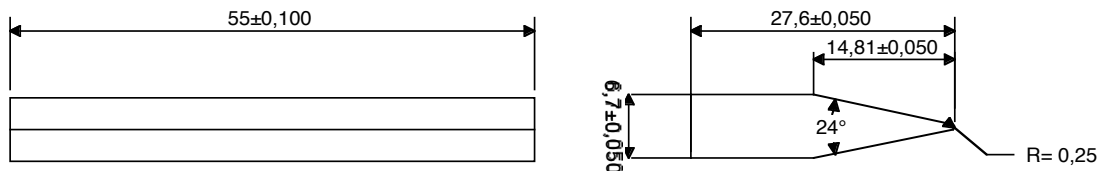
Eprouvette standard de fatigue thermique type FT-S.
